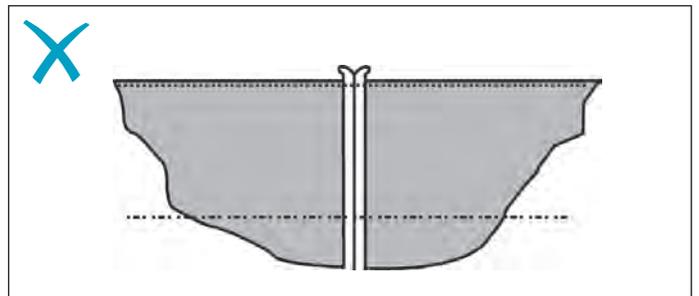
Cordón de soldadura (insuficiente)
